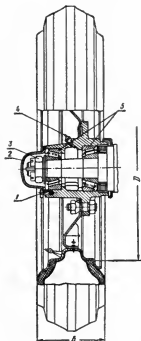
Регулировка подшипников направляющего колеса трактора «Беларусь»:
